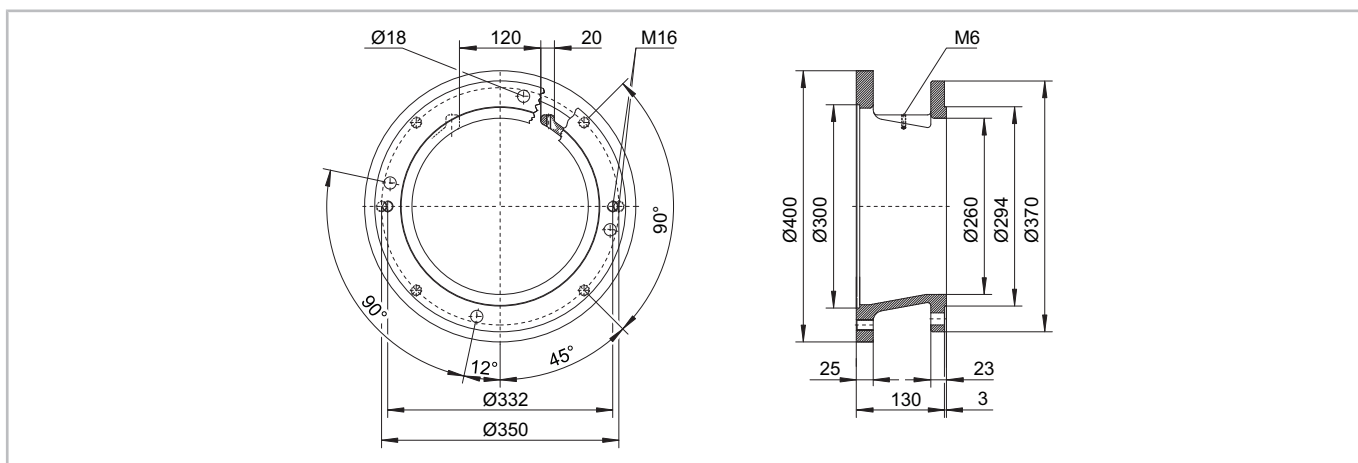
Габаритный чертеж кожуха муфты GS7090
